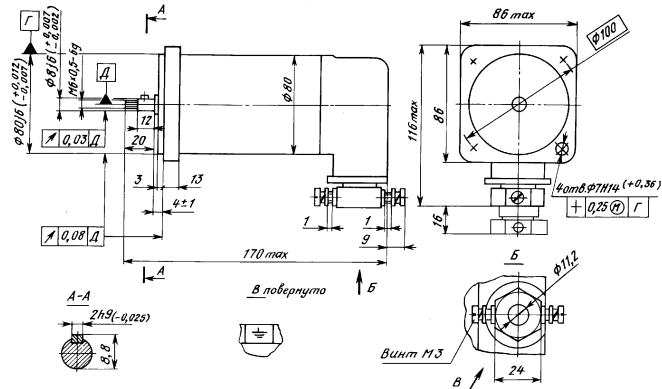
Габаритные, установочные и присоединительные размеры электродвигателей ДАТ53172, ДАТ53172-2, ДАТ53182, ДАТ53182-2:
